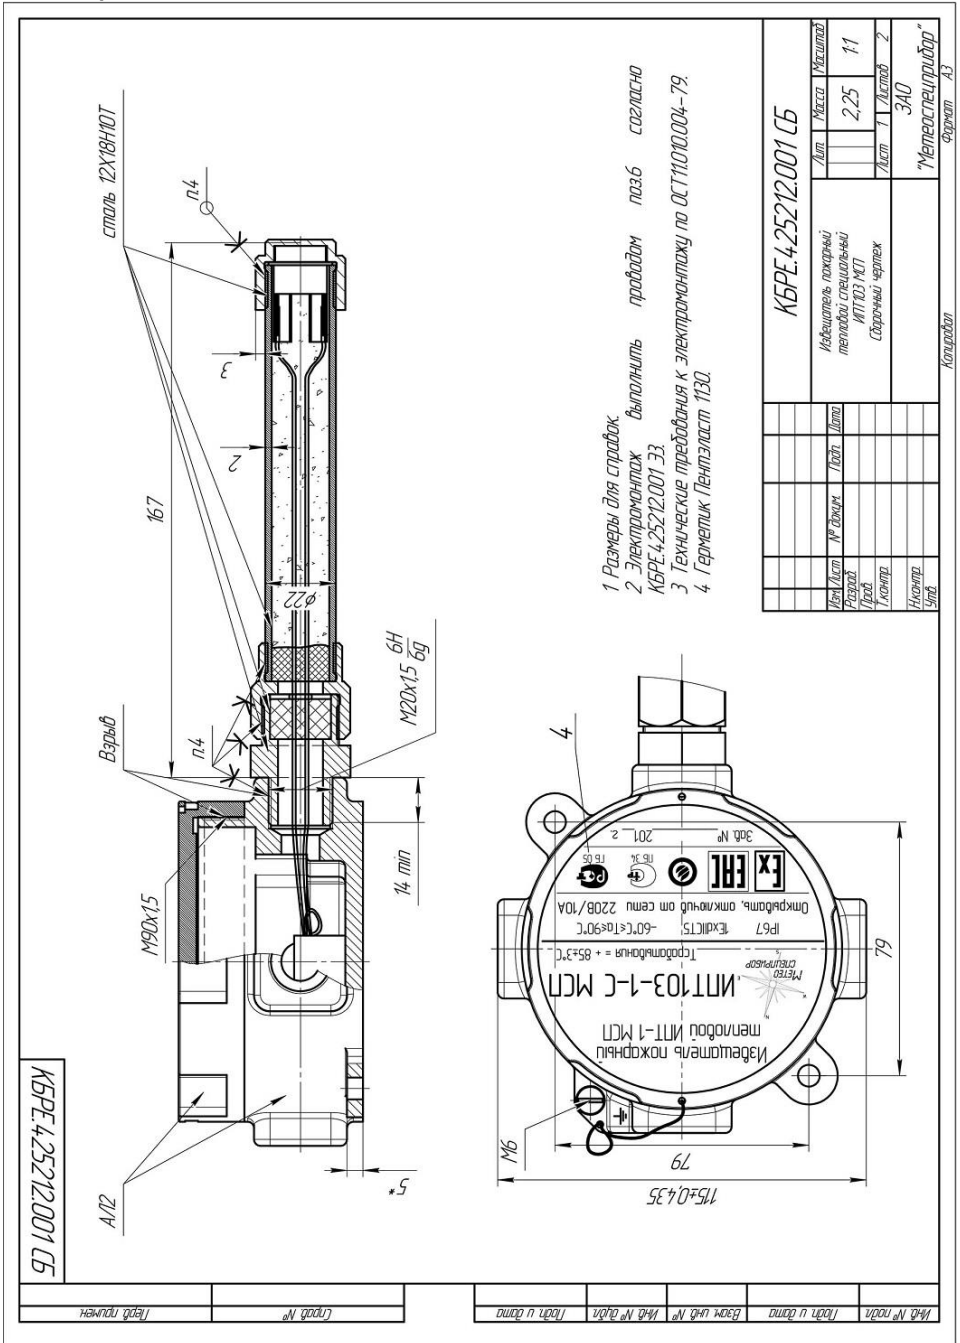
Сборочный чертёж извещателя пожарного теплового ИПТ-103 МСП
